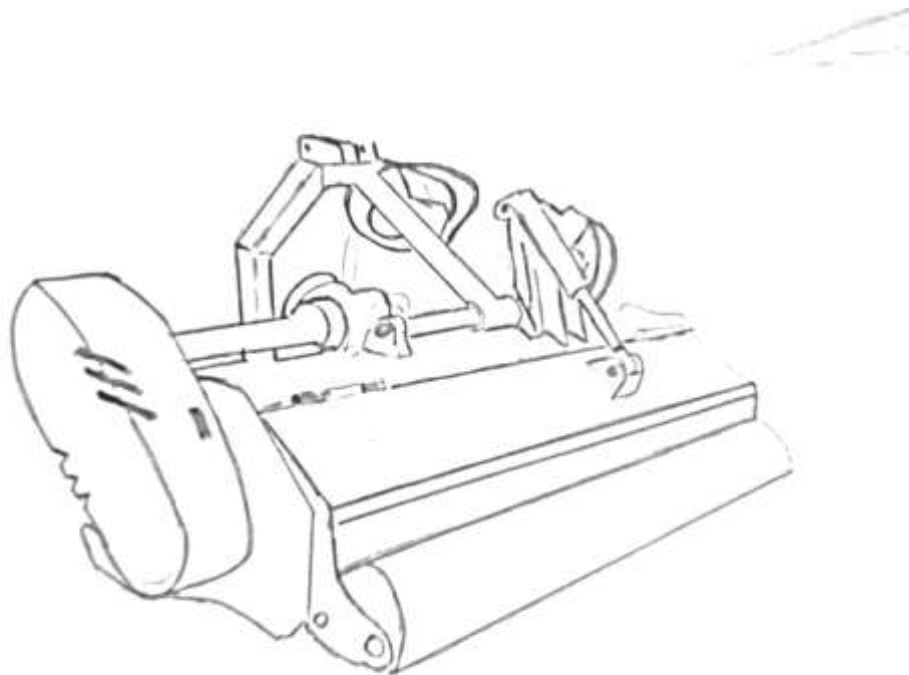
Vista Isométrica de máquina trituradora F2N- DRAA,
